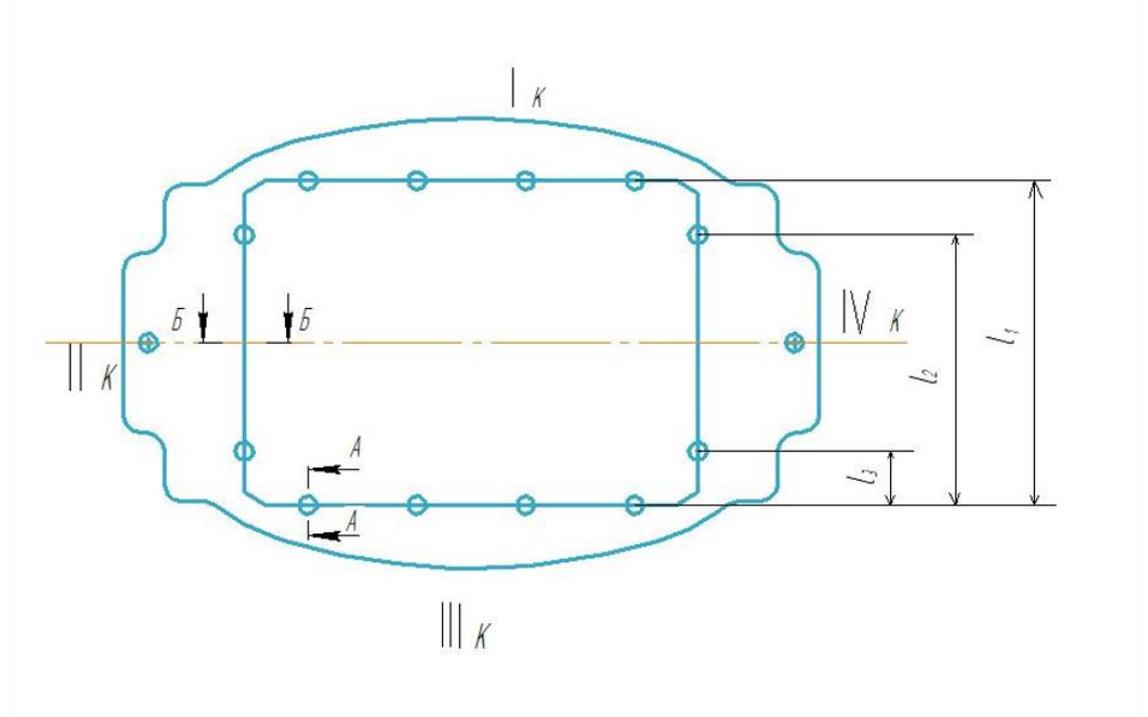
Конструкция стыка обечайки корпуса МКА с ТСП1
